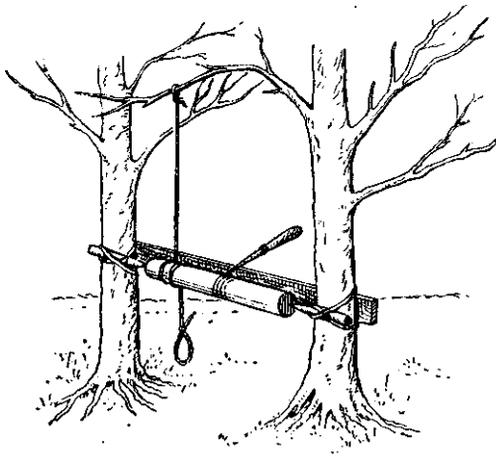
Прimitивный токарный станок с ножным веревочным приводом.
